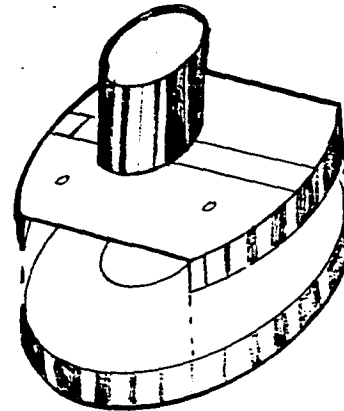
plantilla para trazado de modulos y barrenado (pieza similar para barrenado en reloj, espejo mesa de centro y portarretratos).
